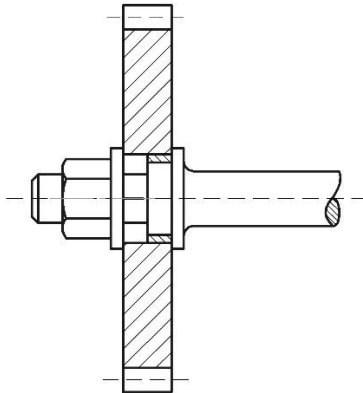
Посадка зубчатого колеса с распорной втулкой меньшей ширины
